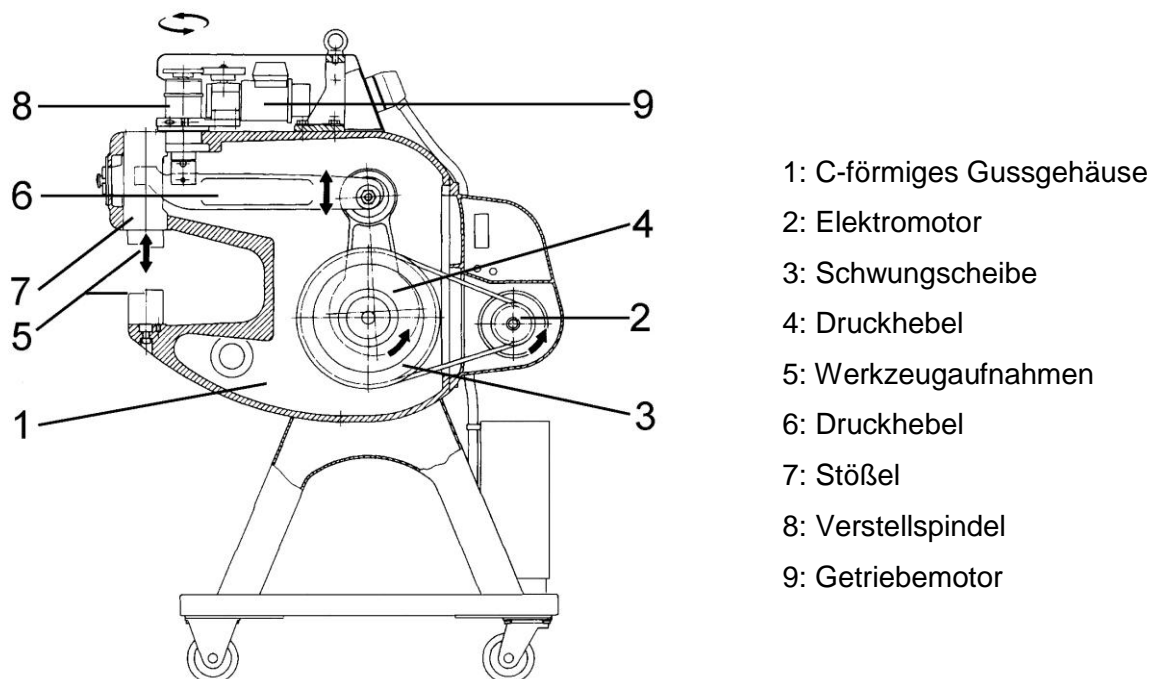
Baugruppen Eckold Kraftformer KF 330 [Quelle: Eckold]
